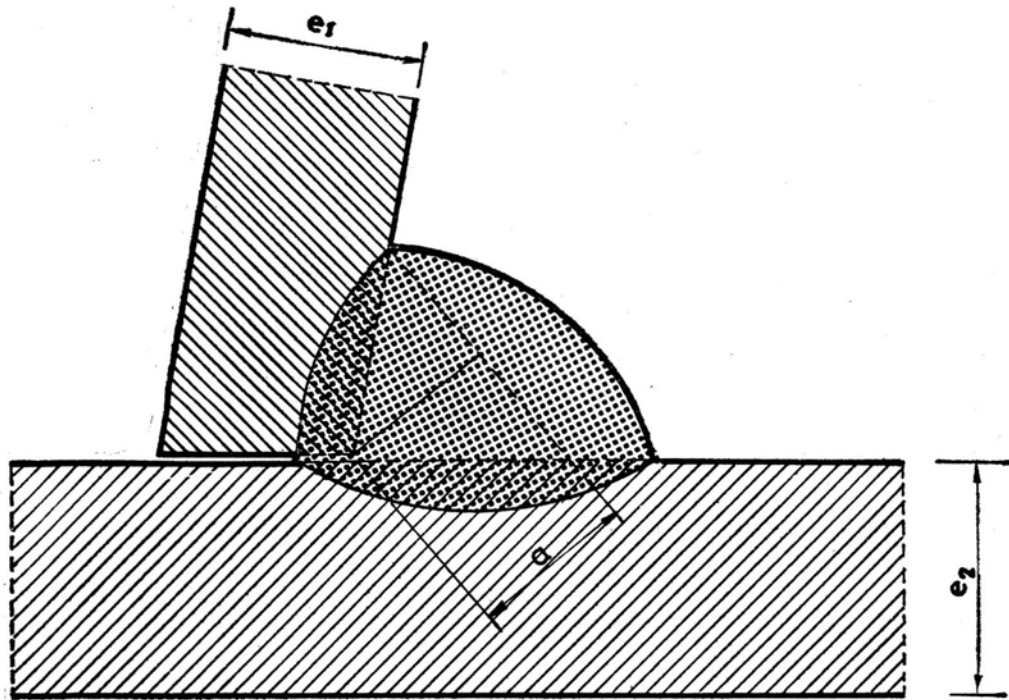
GARGANTA a DE UNA SOLDADURA EN ANGULO
